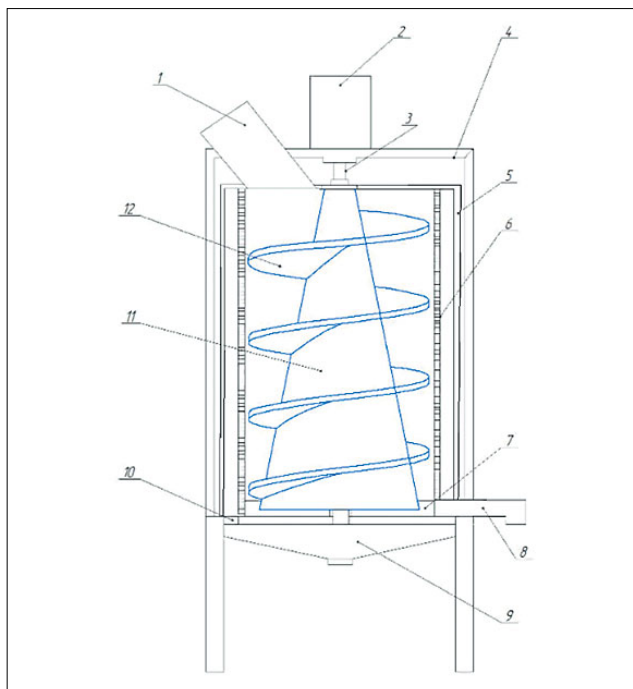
Схема протирочной машины: 1 – загрузочный патрубок; 2 – электродвигатель; 3 – вал; 4 – корпус; 5 – корзина; 6 – ситовой барабан; 7 – ворошитель; 8 – разгрузочный лоток; 9 – сборочный бункер; 10 – отверстия для прохождения протертого сырья; 11 – конус (шнековый вытеснитель); 12 – лопасти
